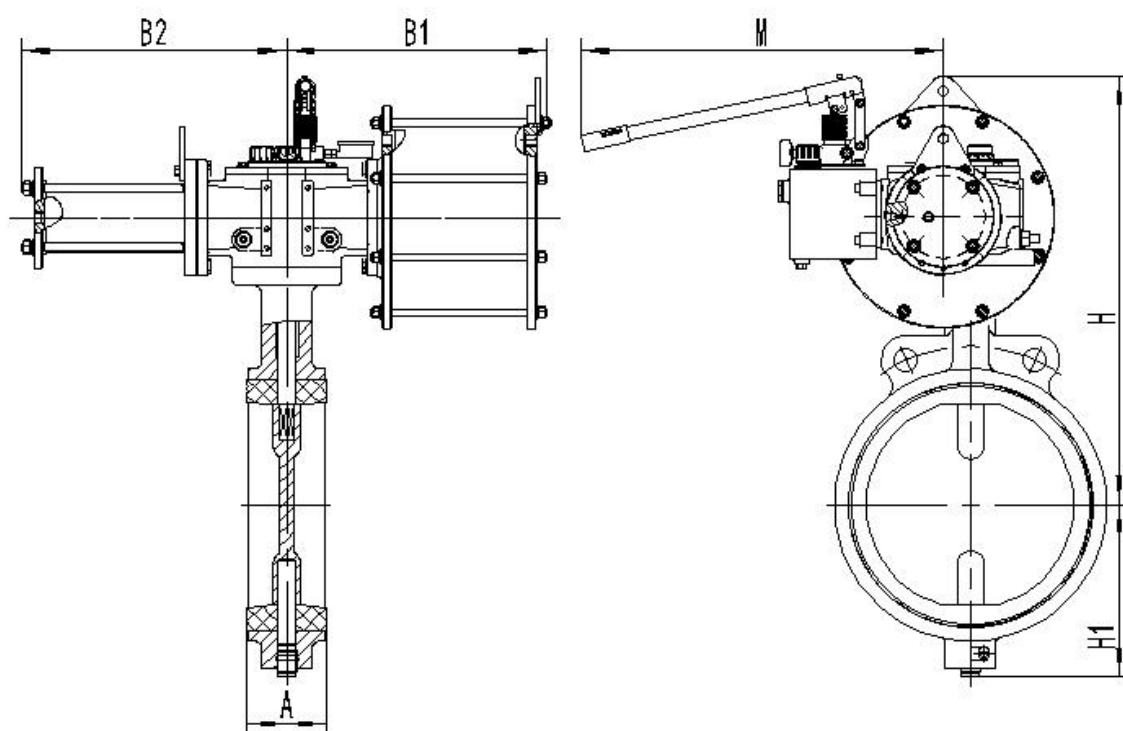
配 HCW40D004~HCW50D005 带液压手轮外形尺寸图
